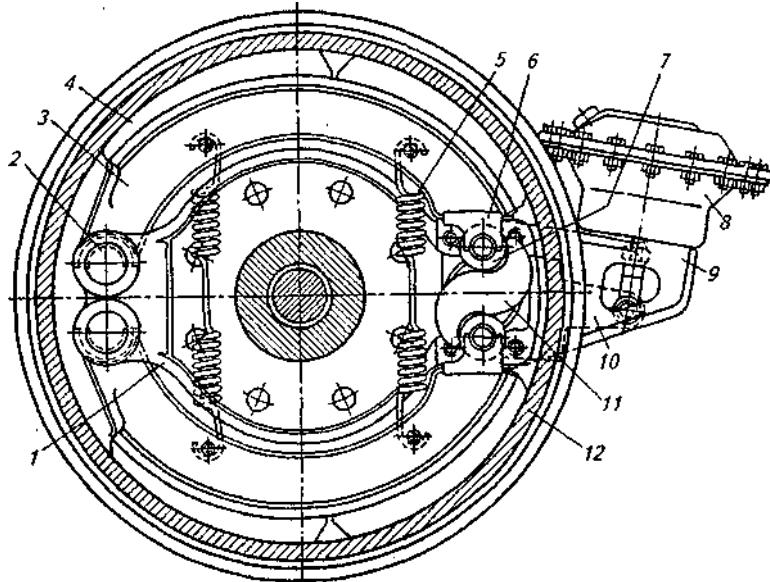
Барабанный тормозной механизм: 1 — суппорт; 2 — опора колодки; 3 — колодка; 4 — фрикционная накладка; 5—оттяжная пружина; 6— опора ролика; 7- ролик; 8— тормозная камера; 9- кронштейн тормозной камеры; 10— регулировочный рычаг; 11 — разжимной кулак; 12— тормозной барабан.
